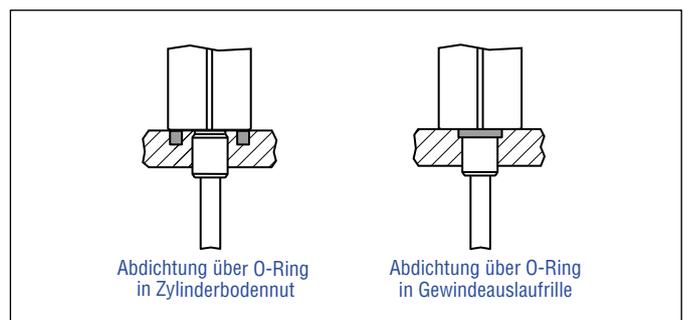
Möglichkeiten der Abdichtung für Gewindeflansch mit flacher Flanschfläche
